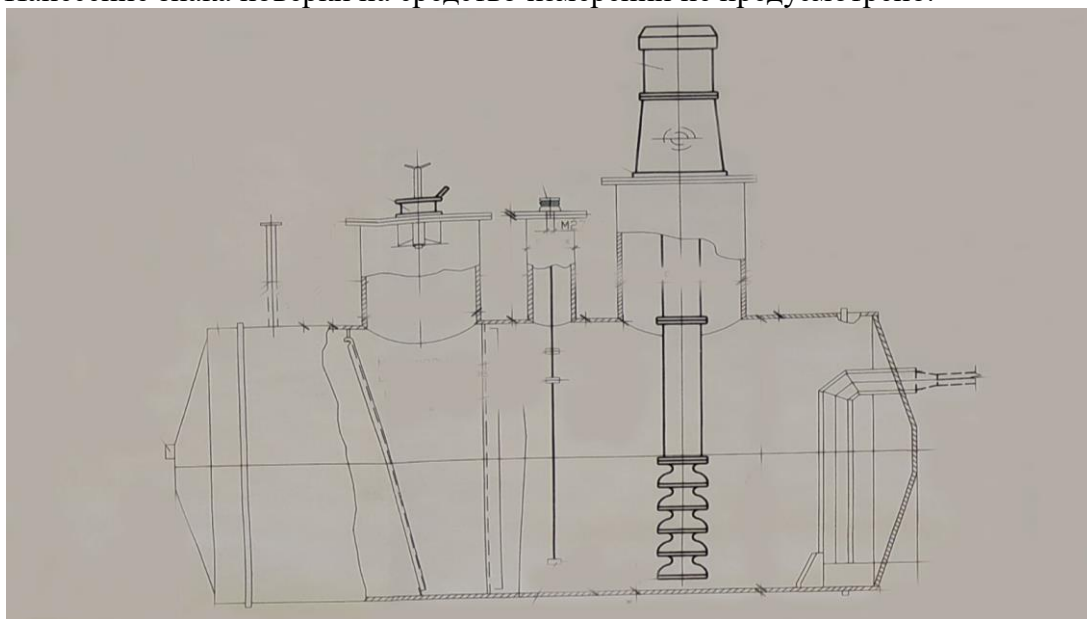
Общий вид эскиза резервуара горизонтального стального цилиндрического ЕП-20
